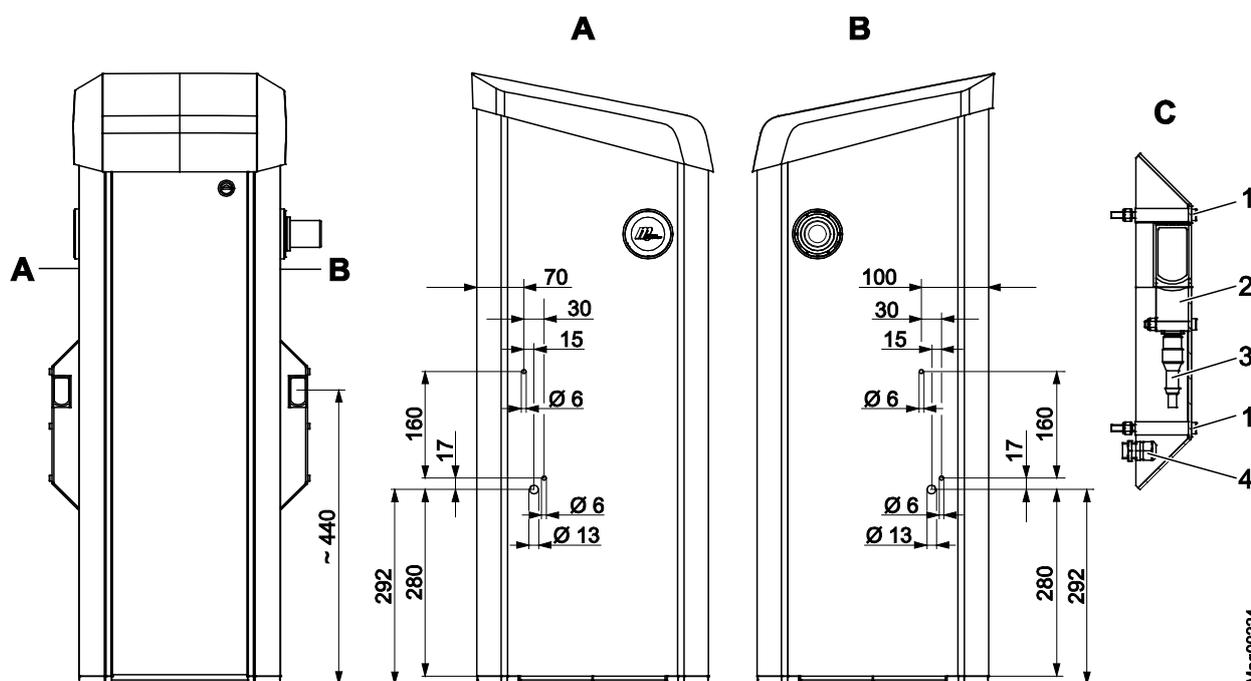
Монтаж корпуса фоторелейного барьера передатчика на стойке шлагбаума
